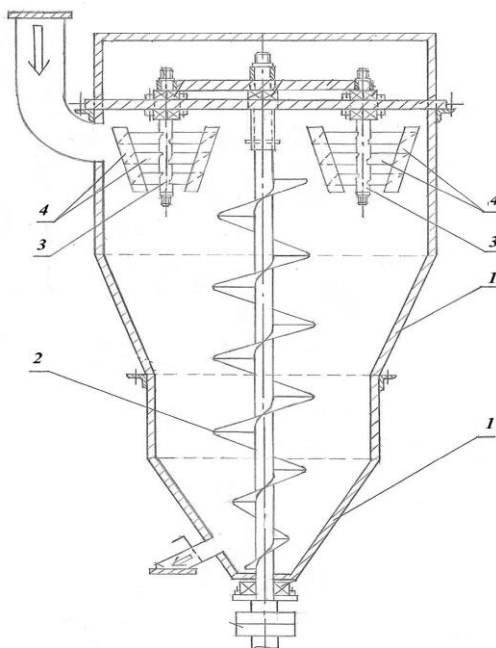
Конструктивна схема вертикального змішувача інгредієнтів комбікормів: 1 – корпус змішувача; 2 – робочий орган у вигляді шнека; 3 – консольні вали; 4 – двохплощинні лопатки.
